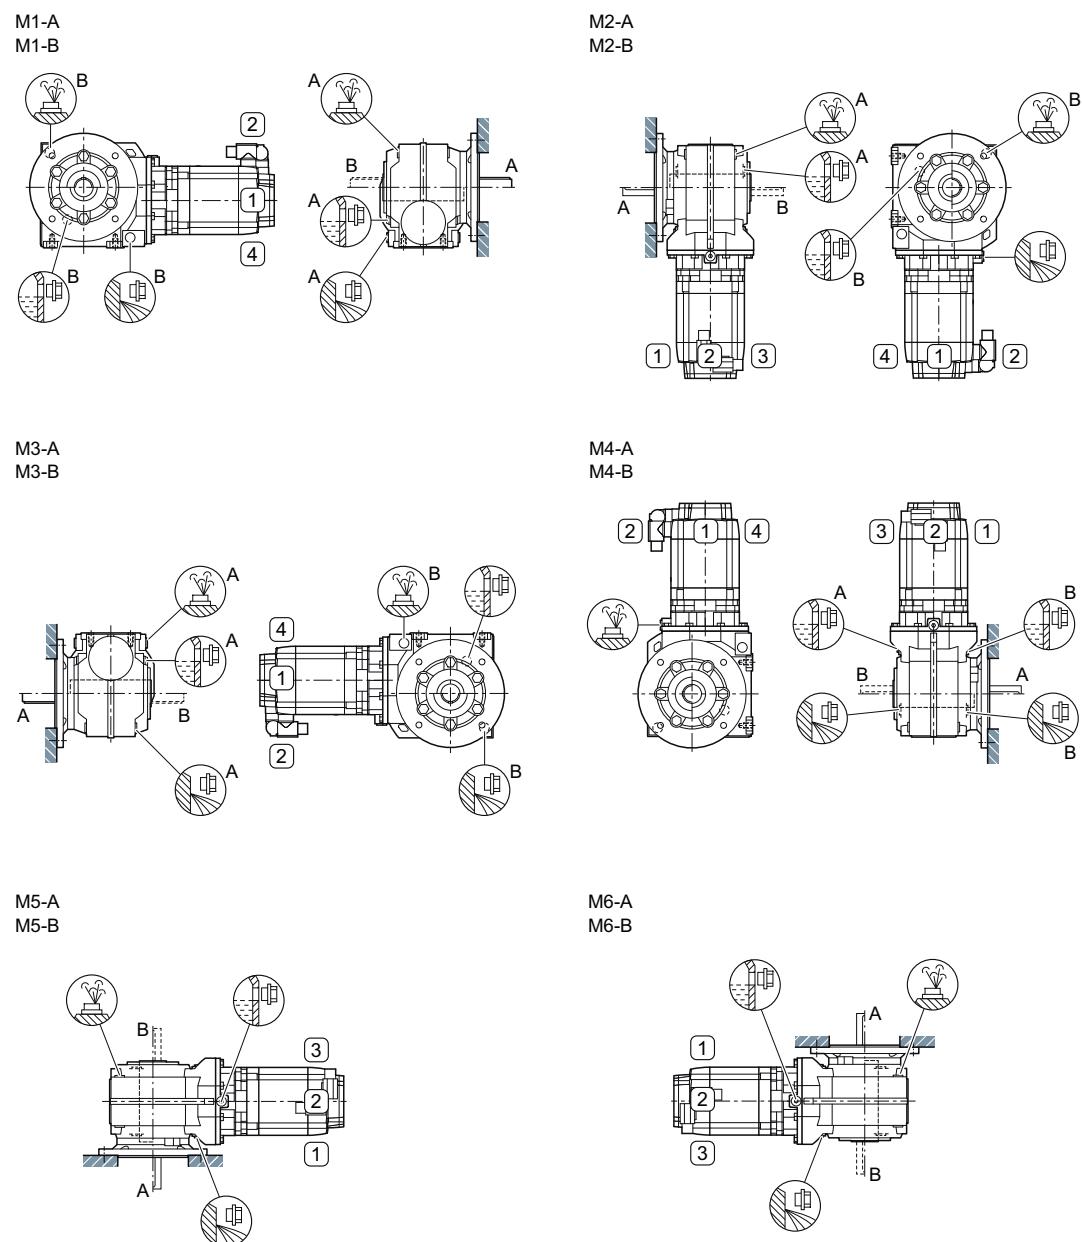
Einbaulagen für Servo-Stirnradschneckengetriebemotor CF (Flanschausführung) und CAZ (Gehäuseflanschausführung), Baugrößen 49 - 89, 2-stufig
